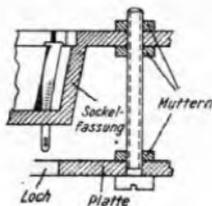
Ist das alte Loch zu klein, läßt sich die Röhrenfassung auf Stützen befestigen
